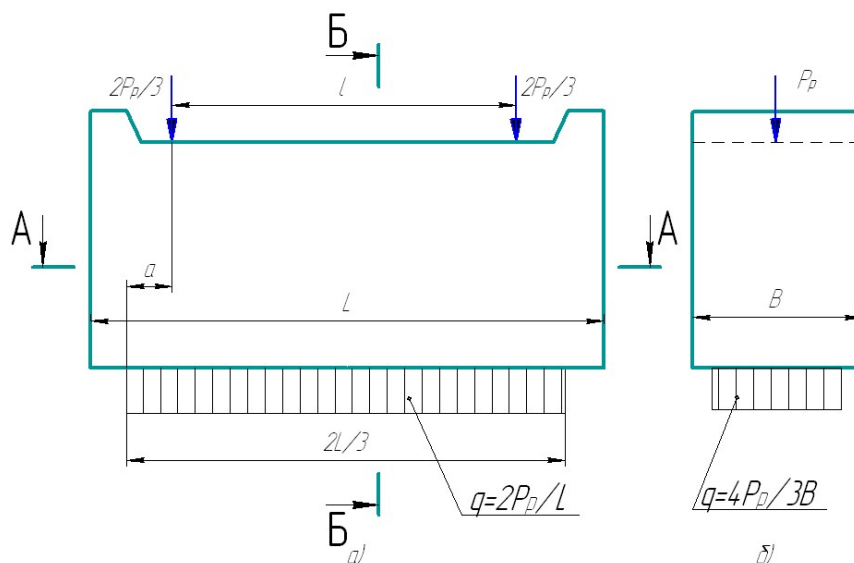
Розрахункова схема повзуна багатокривошипного преса
